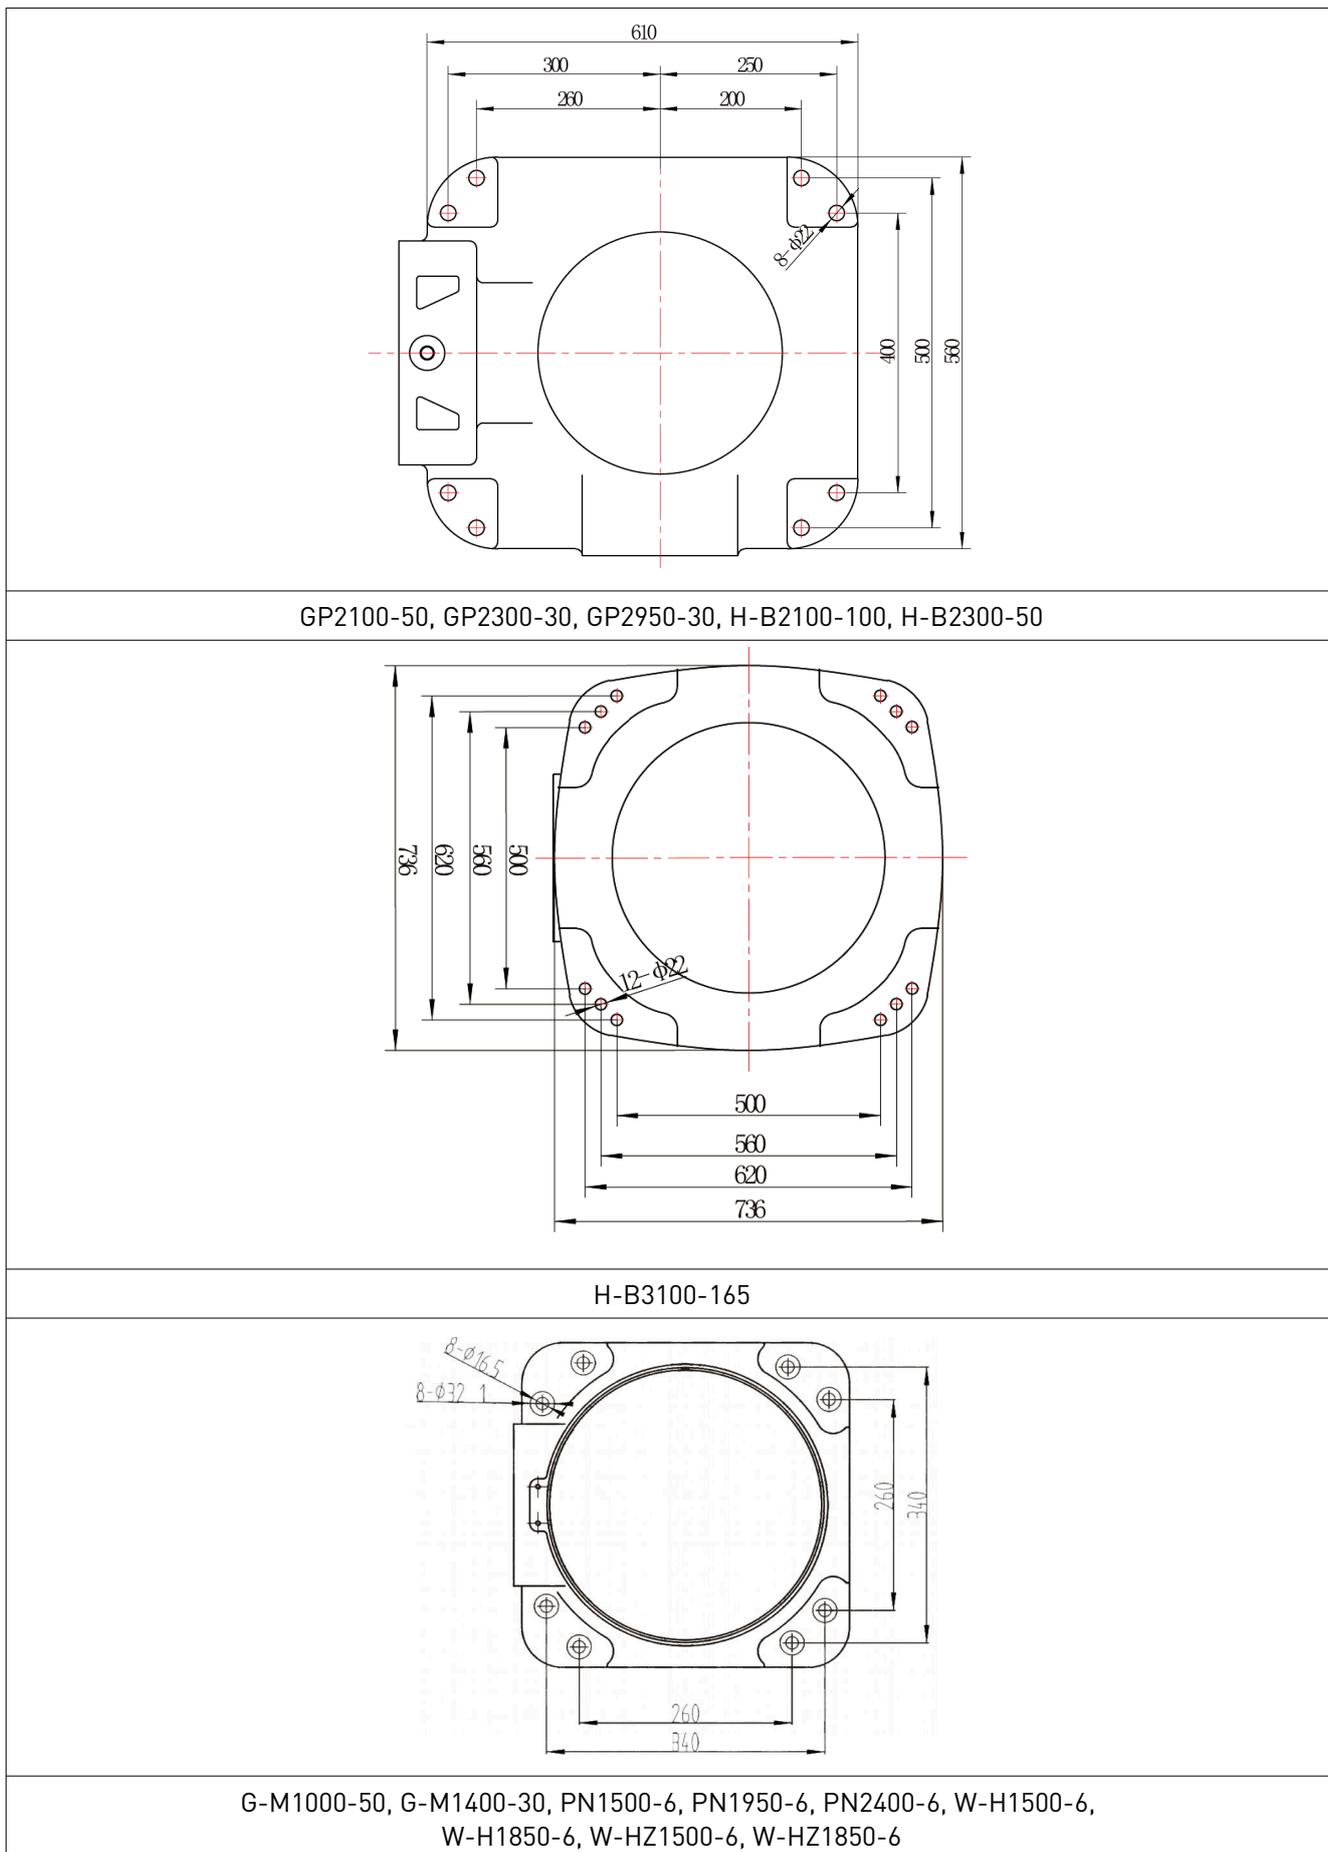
Габаритные и присоединительные размеры основания робота-манипулятора
